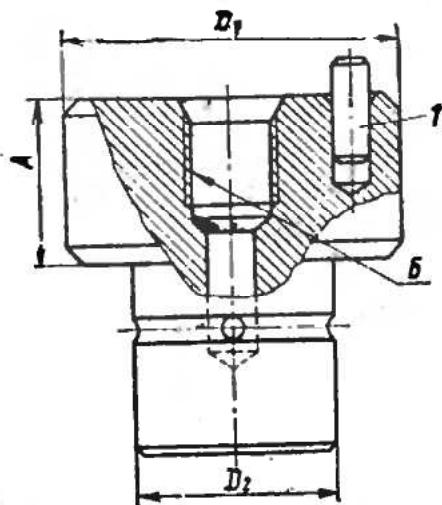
Шкворень поворотного кулака со стопорным штифтом в сборе
